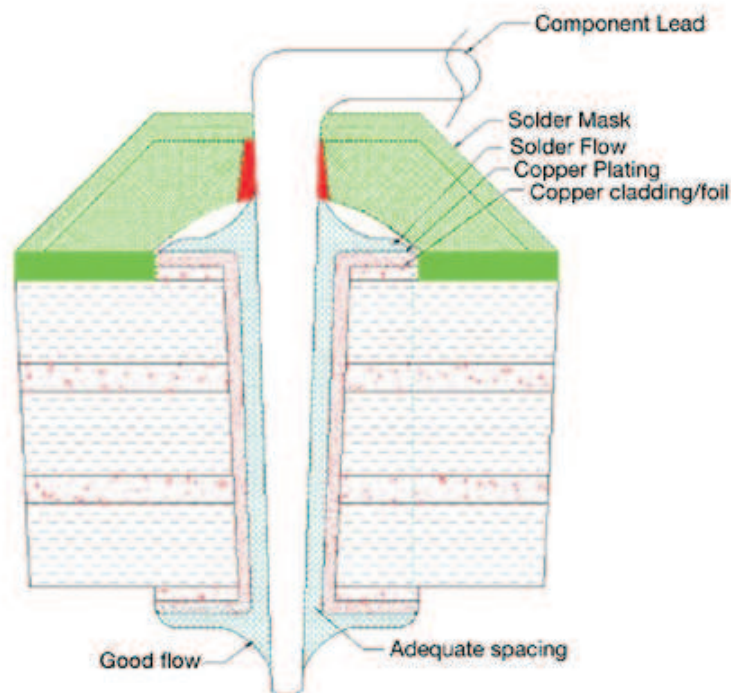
Componente PTH Soldado en una Tarjeta [5].
